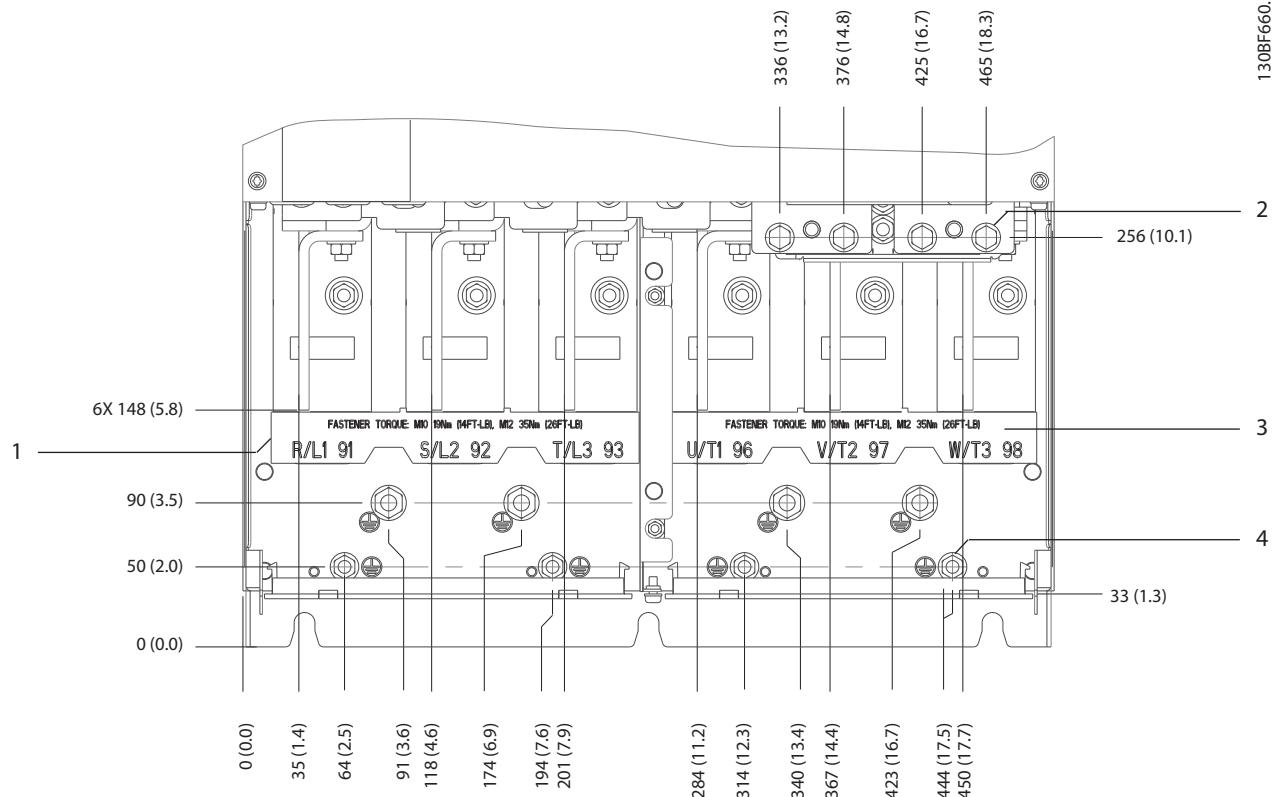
Dimensi Terminal E2h (Tampak Samping)
